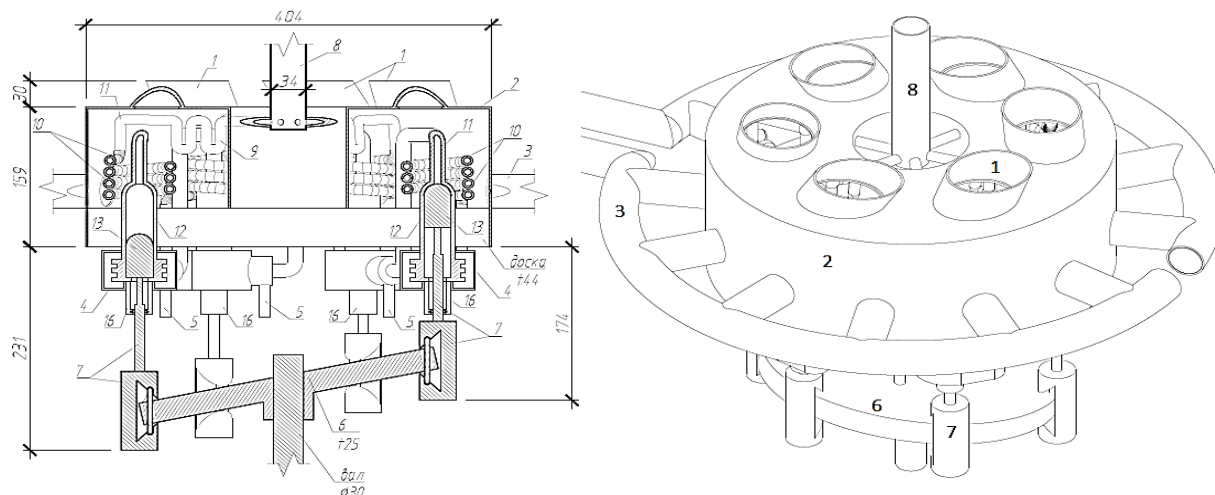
Чертеж двигателя Стирлинга вид сбоку с разрезом (слева) и общий вид (справа)
